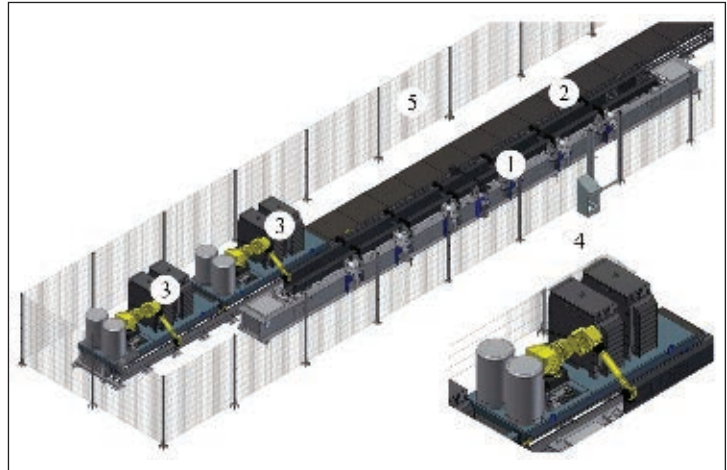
Установка для сварки внутреннего шва хребтовой балки: 1 — стенд; 2 — транспортная система; 3 — платформы с роботами и сварочными источниками питания; 4 — пульт управления; 5 — ограждение
